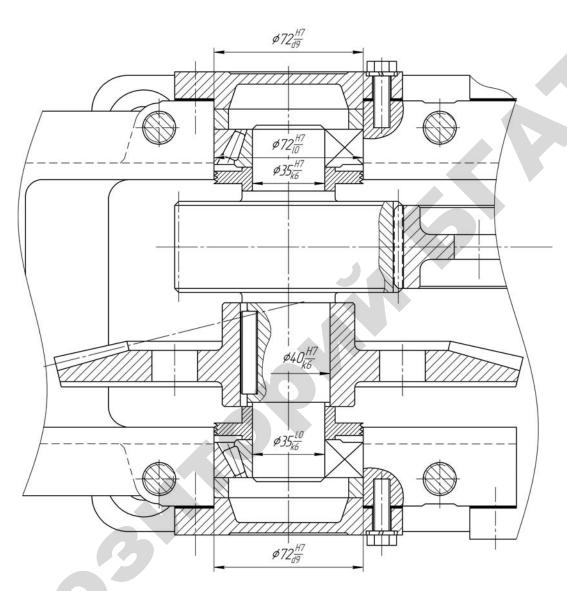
Фрагмент сборочного чертежа двухступенчатого коническо-цилиндрического редуктора
